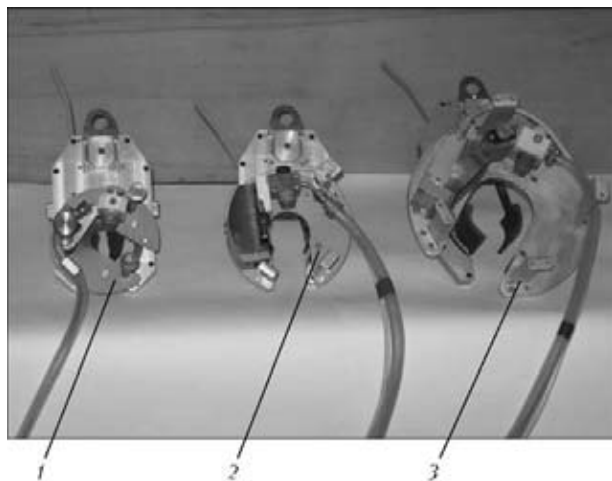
Внешний вид головок сварочных: 1 — АДЦ 627.03.00.000; 2 — АДЦ 625.03.00.000; 3 — АДЦ 626.03.00.000
